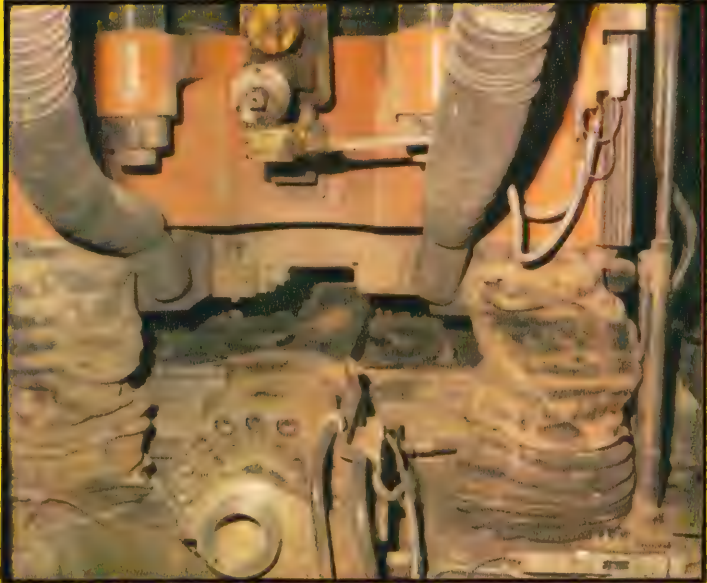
Das Steuerpult der ersten Sprengstoff-Explosivumformmaschine (Abb. 1) der Welt...
